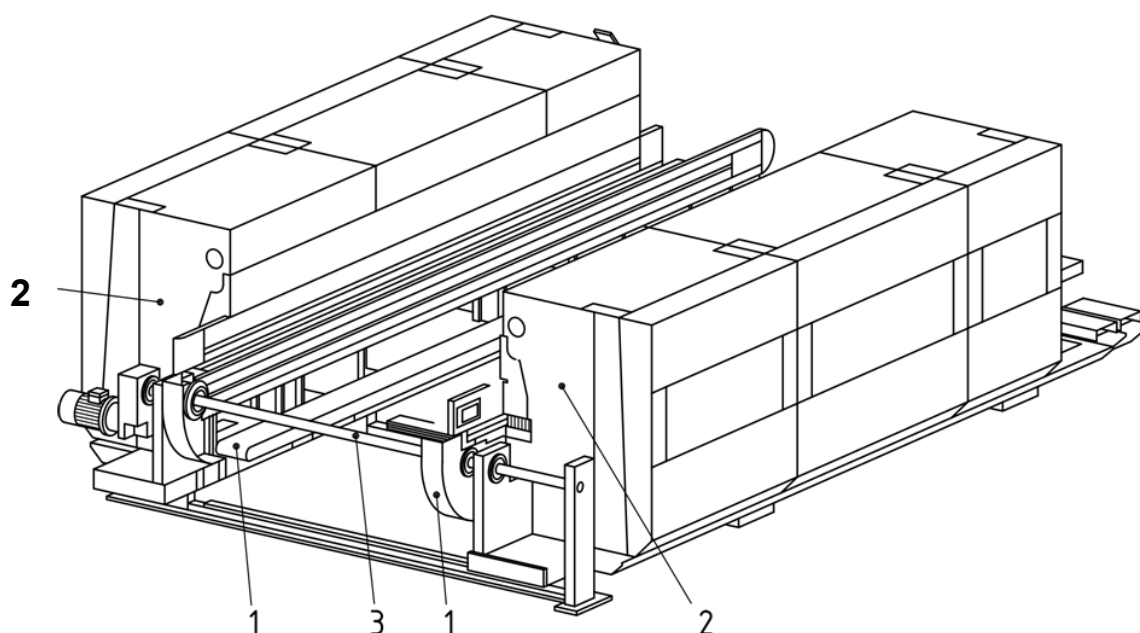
Пример устройства автоматического возврата заготовок для одностороннего станка
